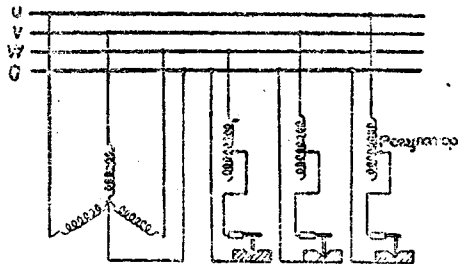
Схема многопостовой сварки на переменном токе
